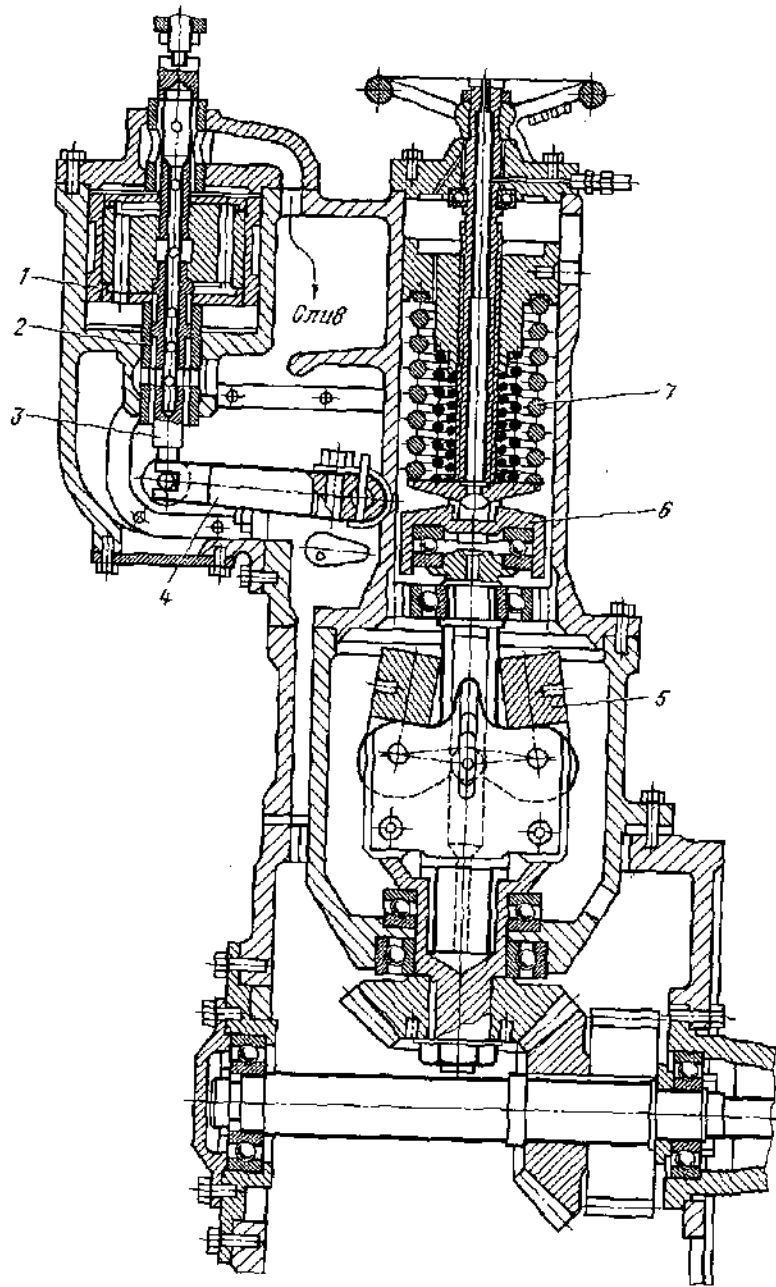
Конструктивный разрез регулятора фирмы МАН двигателей KZ57/80:
